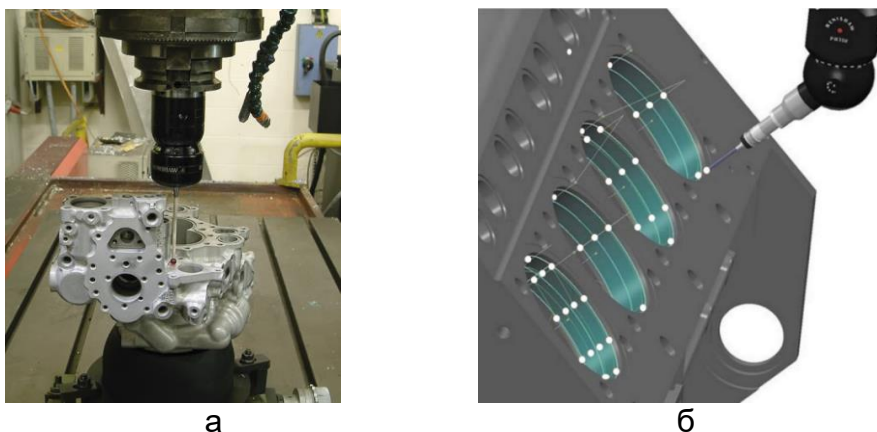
а – вимірювання корпусної деталі на верстаті з ЧПК,
